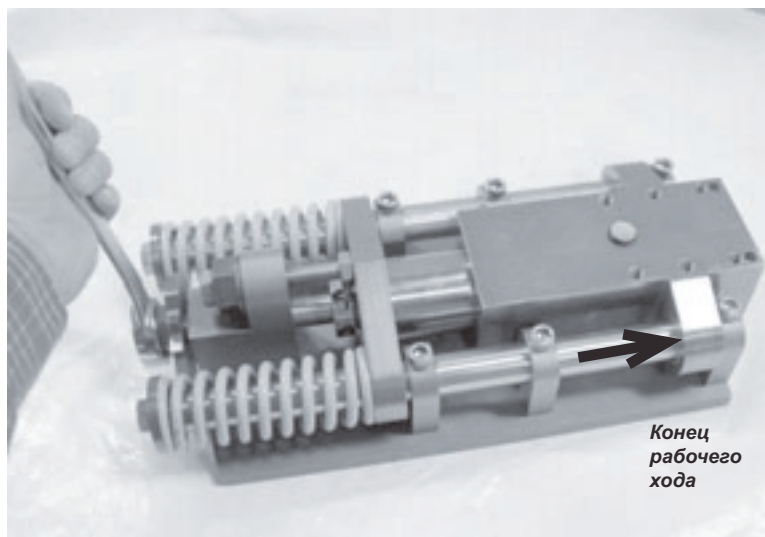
Поверните подающую гайку звездочки против часовой стрелки для перемещения суппорта к концу рабочего хода.
